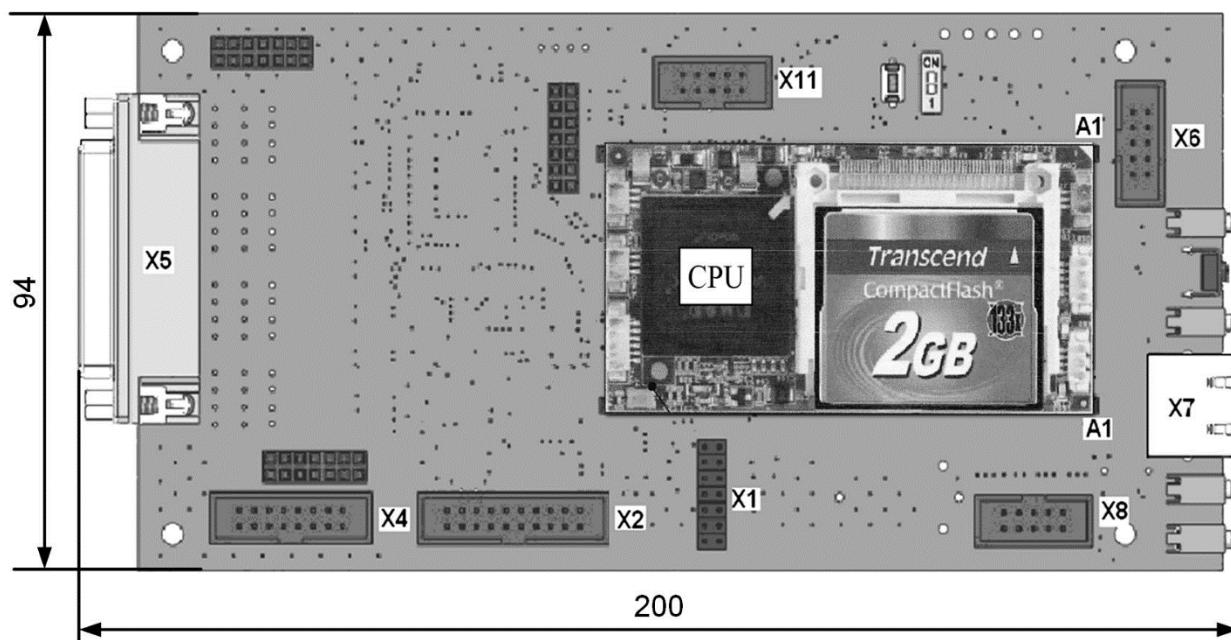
Внешний вид и габаритные размеры платы DCN-Q4E
